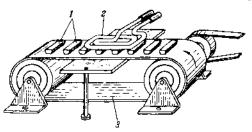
Схема конвейерного устройства для пайки металлических коробок: 1— коробок, 2— нндуктор, 3— асбестовая лента конвейера
